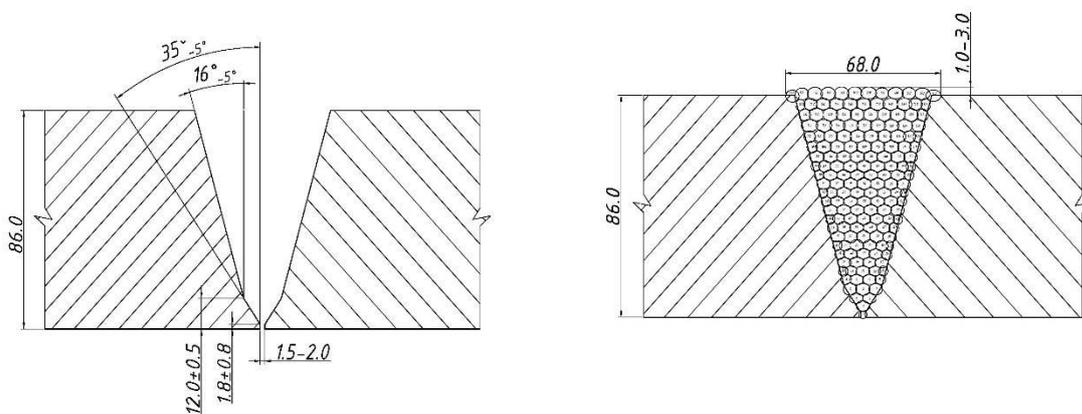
Конструкция соединения и конструктивные элементы сварного шва
